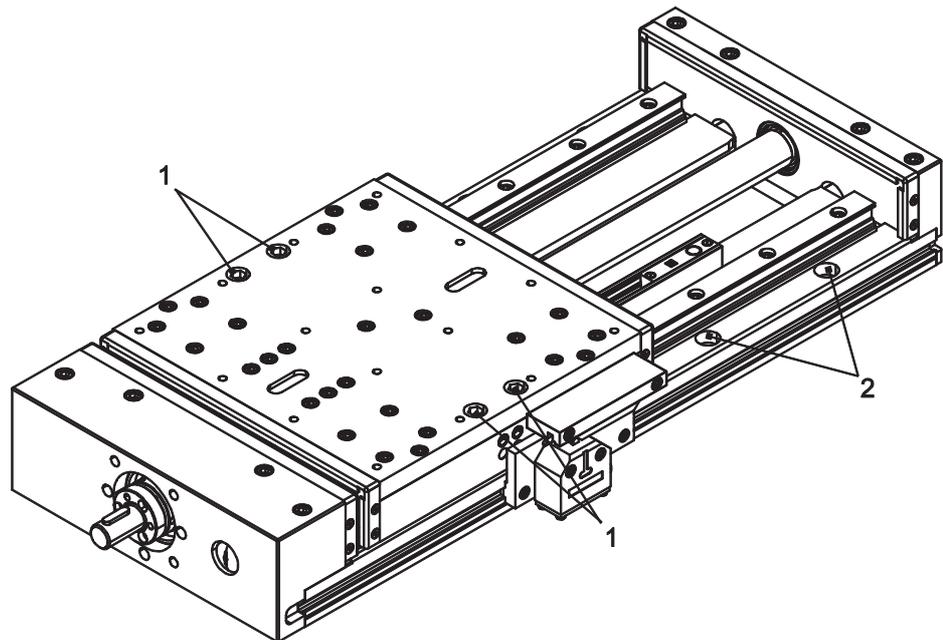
Montagebohrungen mit Gewindestift (1) und Befestigungsbohrungen (2)
